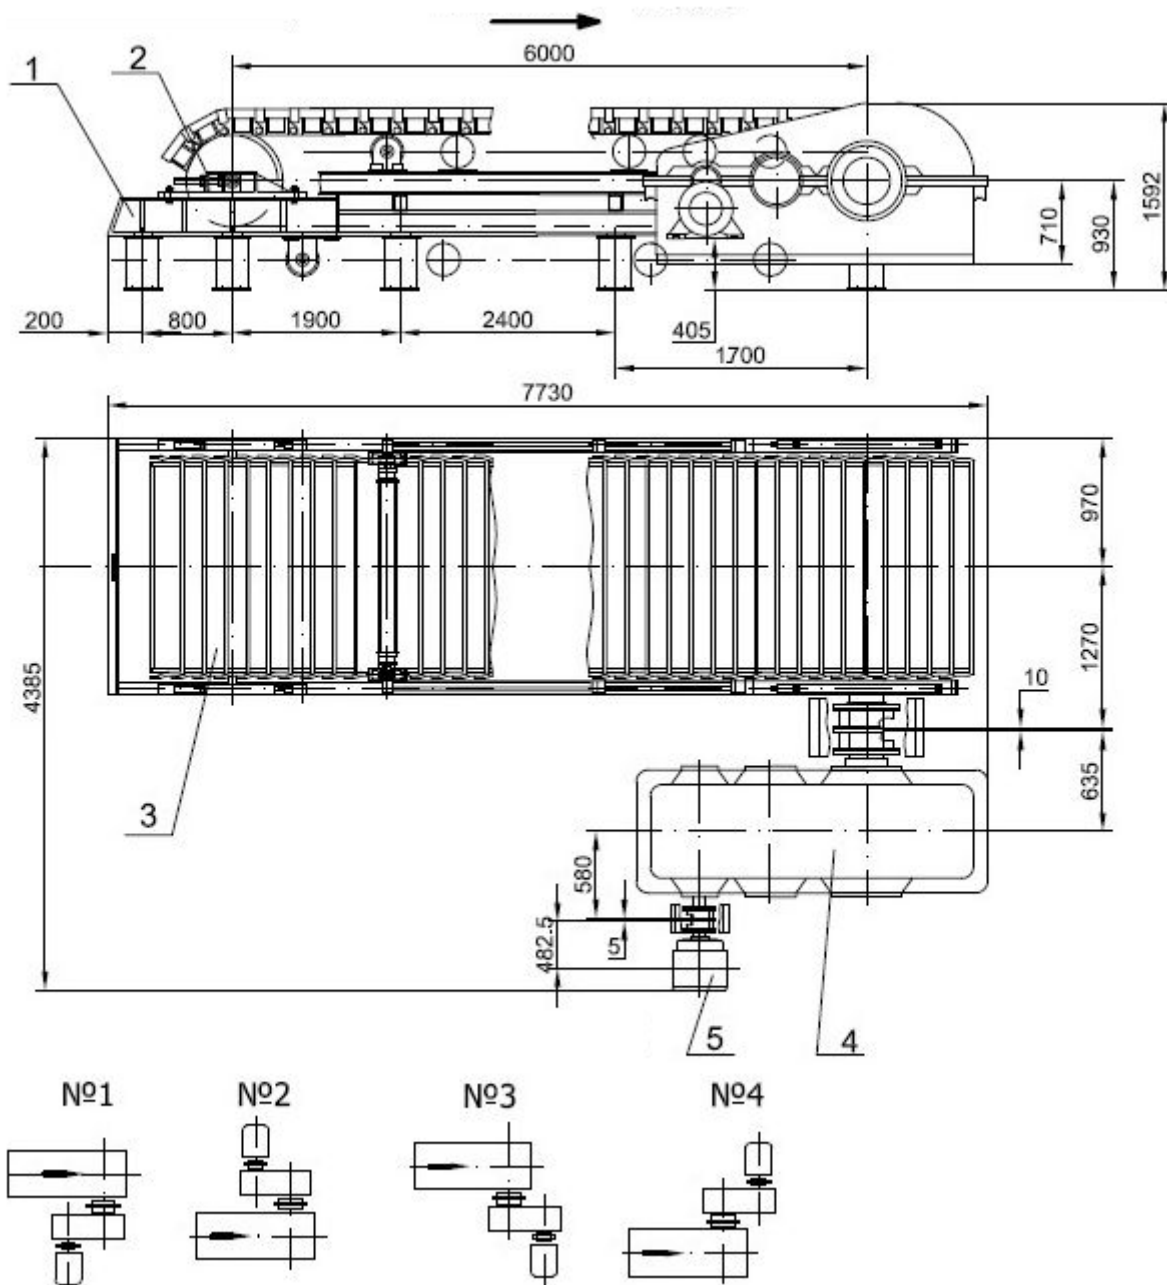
Пластинчастий живильний ПП-1-15: 1 – рама живильника; 2 – пристрій натяжний; 3 – стрічка живильника; 4 – редуктор; 5 – електродвигун [Ошибка! Источник ссылки не найден.]
